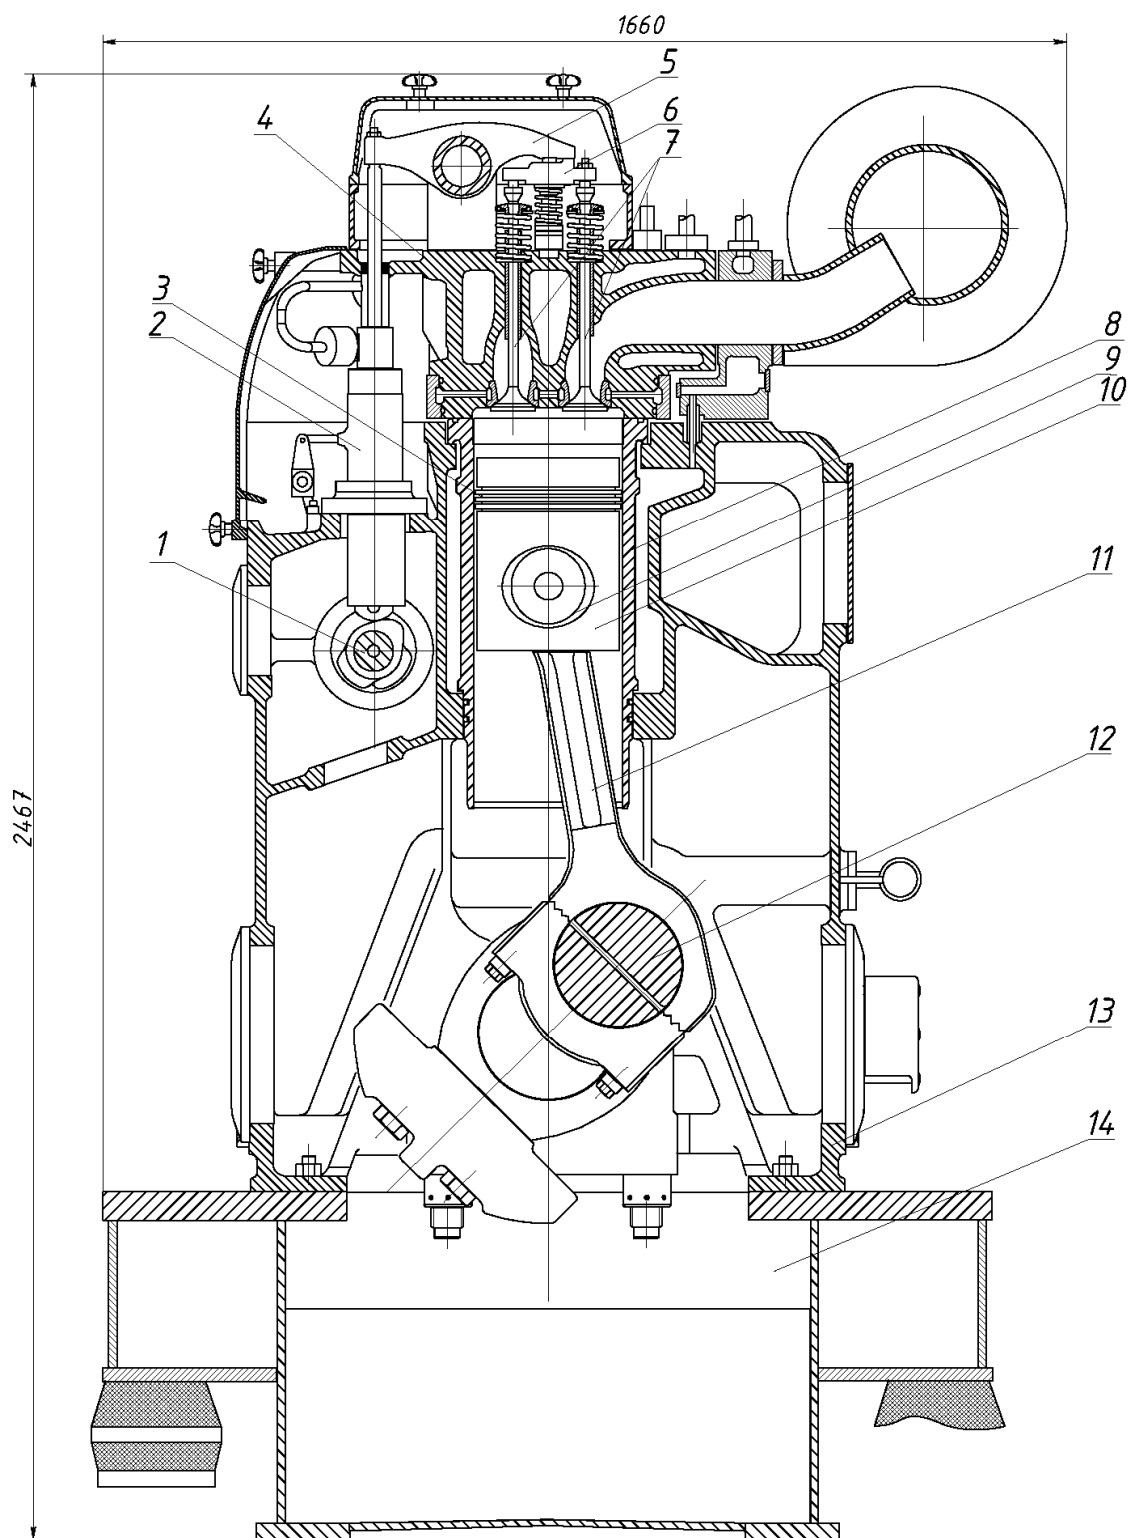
Загальне компонування суднового чотиритактного високооборотного двигуна L23/30: 1 – розподільний вал привода клапанів та ПНВТ; 2 – ПНВТ; 3 – поршневі кільця; 4 – кришка циліндра; 5 – коромисло; 6 – штанга штовхача випускного клапана; 7 – випускний клапан; 8 – гільза циліндра; 9 – поршковий палець; 10 – поршень; 11 – шатун; 12 – колінчатий вал; 13 – картер; 14 – кришка картера;
